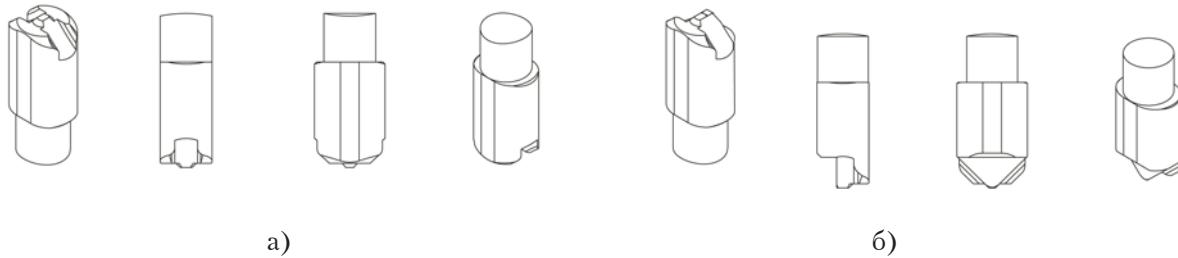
Зовнішній вигляд штифта Integrator™ (а – двобічний; б – однобічний)
